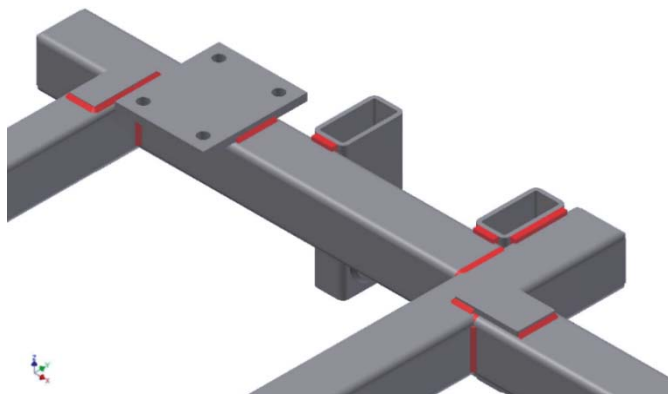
Фрагмент сварной конструкции рамы культиватора
